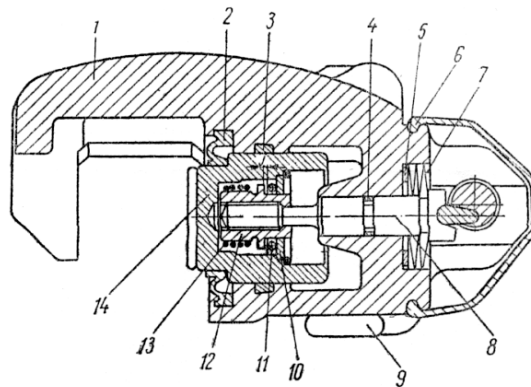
Frâna cu disc deschisă, cu un singur piston de acționare:1-cadru;
